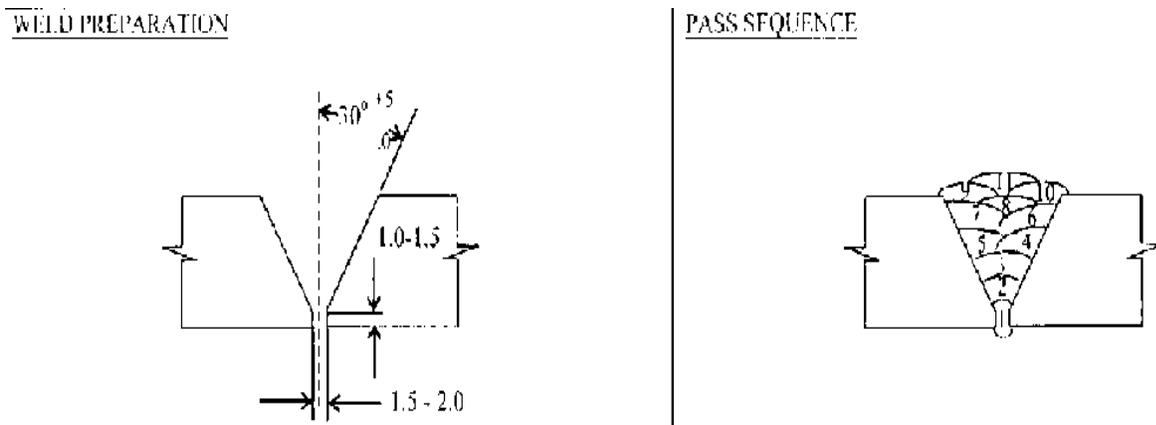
Preparación de la pieza a soldar (izquierda) y secuencia de pasadas (derecha).
